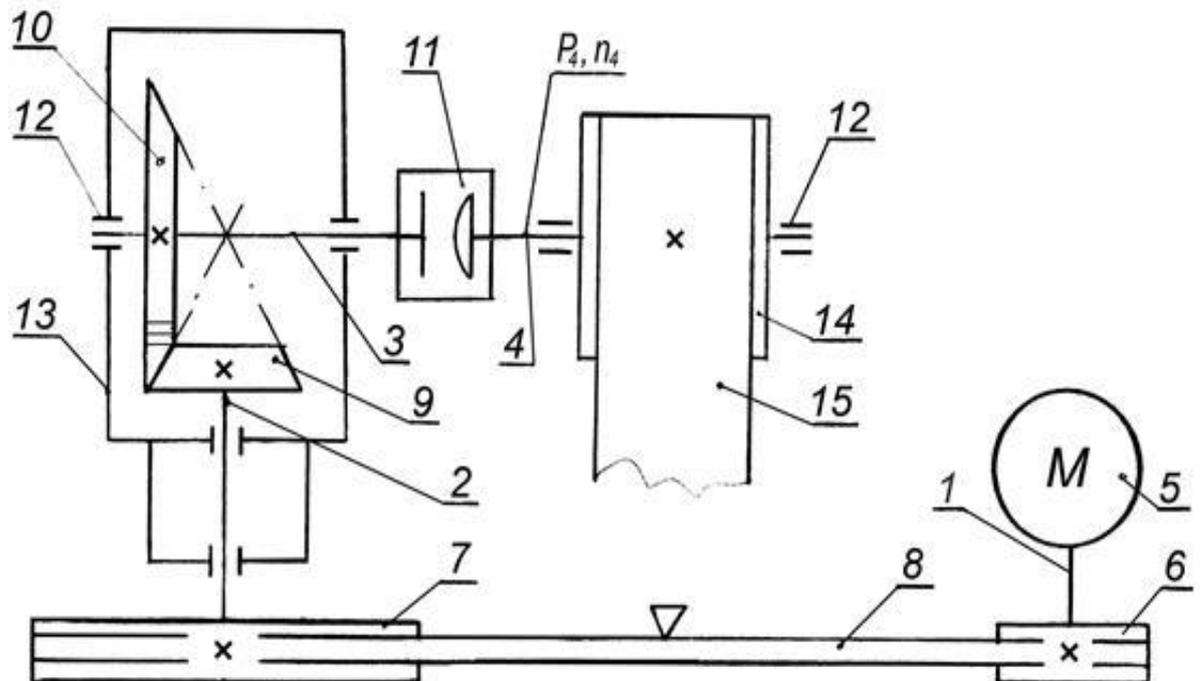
Кинематическая схема привода с применением редуктора с коническим зубчатым зацеплением
